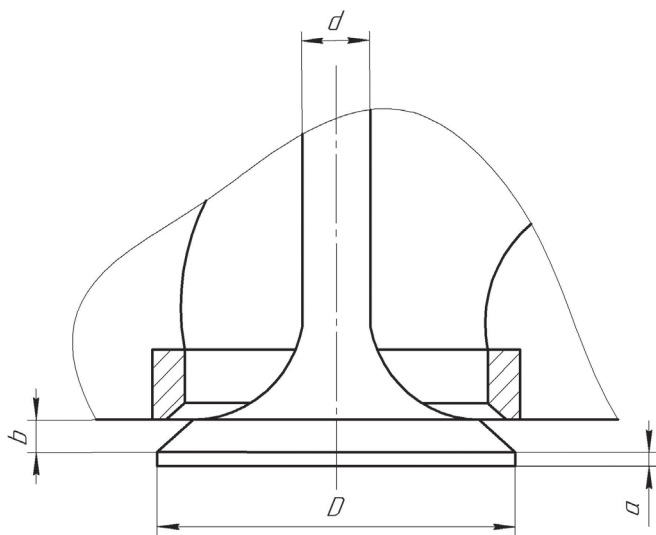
Схематическое изображение профиля рабочей части выпускного клапана: D – диаметр тарелки клапана; a – ширина цилиндрического пояса; b – ширина рабочей фаски; d – диаметр стержня
